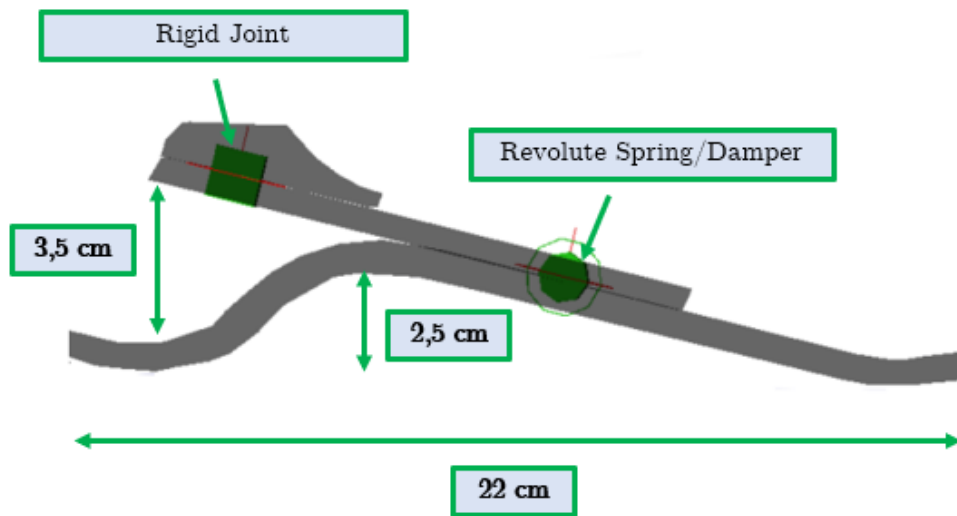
Disegno SimWise 4D piede protesico Walking Foot MP
